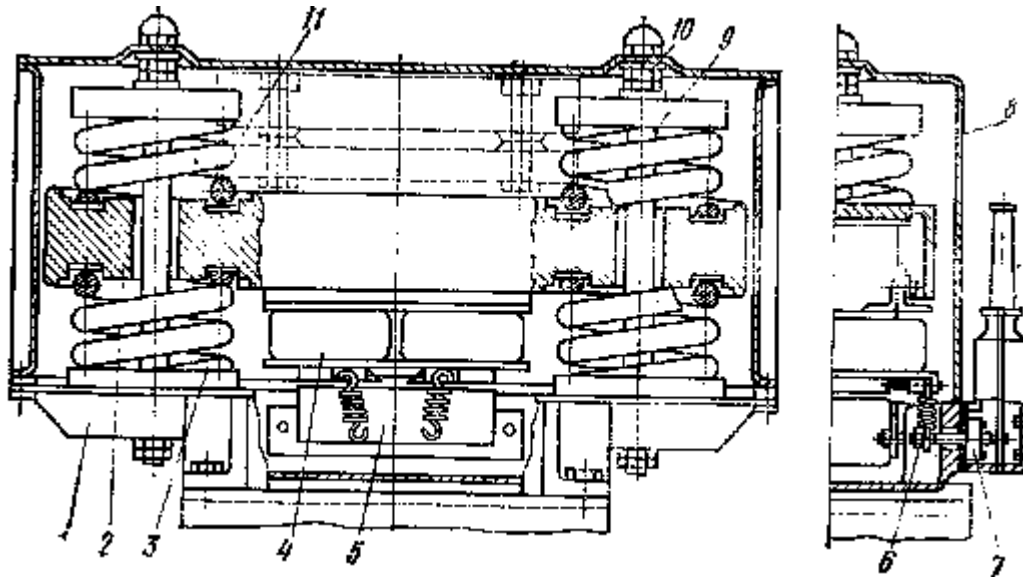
Конструкция одноконтного электромагнитного вибровозбудителя с витыми пружинами сжатия
